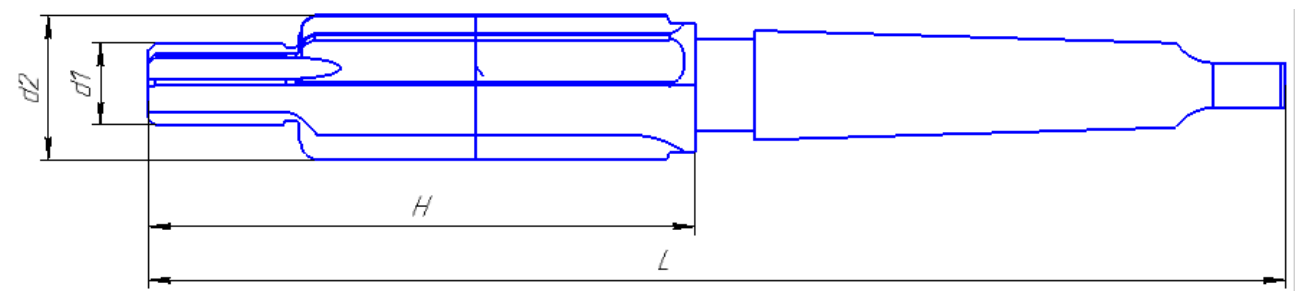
Комбінована двухступінчаста розвертка
